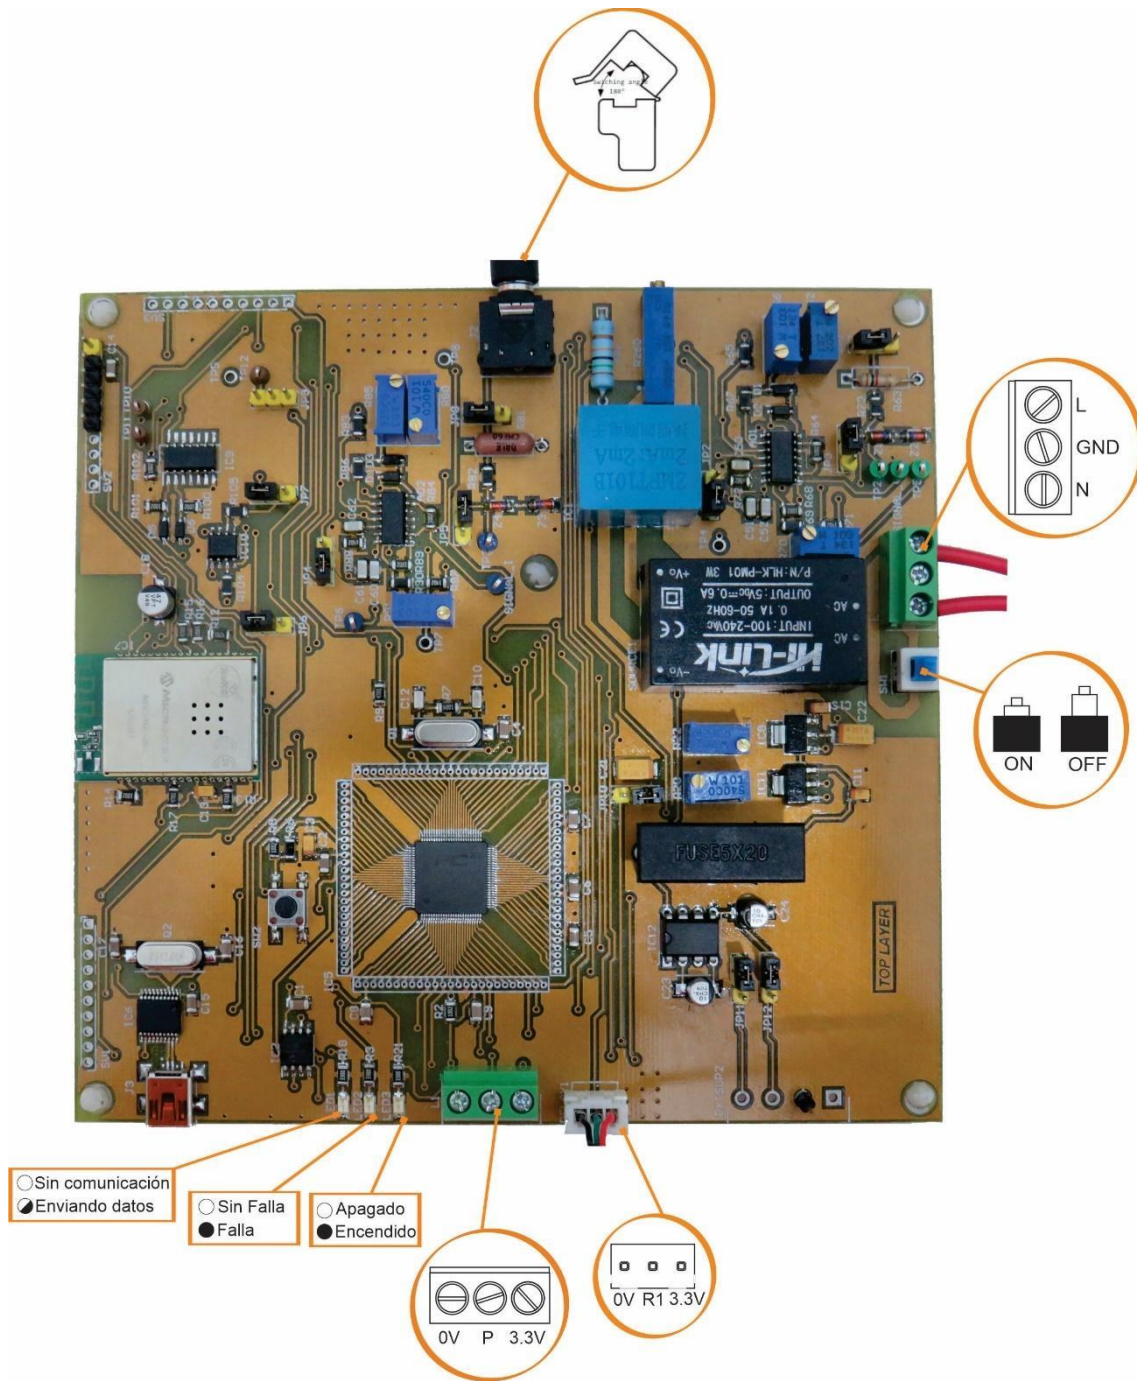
Imagen real de PCB y detalle de componentes de conexión e indicación.
